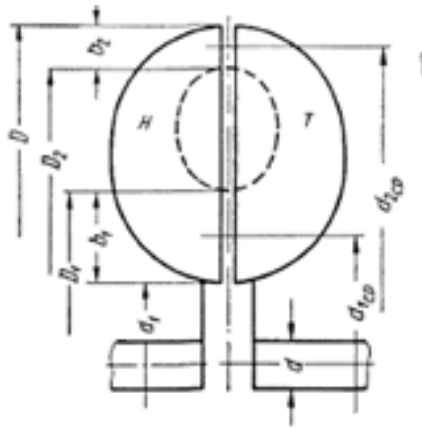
Основні розміри робочого колеса ГМ
